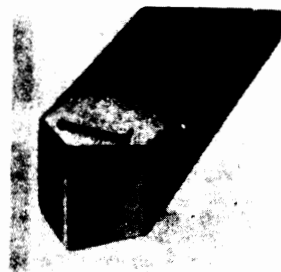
Herramienta sin hoja metálica de soldar lista para la soldadura.
